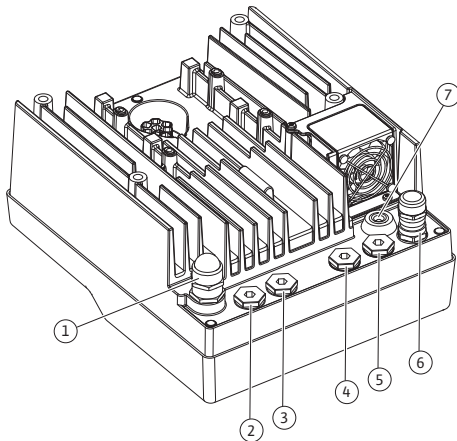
Prensa-cabos/passagens de cabos (0,37 kW – 7,5 kW)
